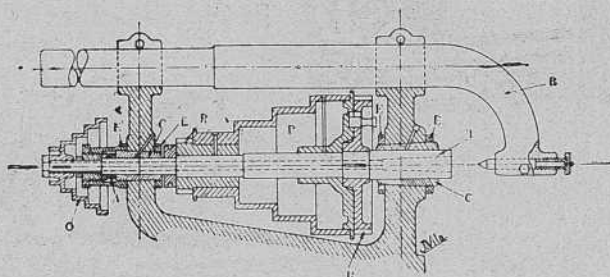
Detalle del cabezal de una fresadora. *B*, brazo; *T*, eje; *C*, cojinetes *E*, tuercas para ajustar los cojinetes; *P*, polea de escalones; *R*, retardo; *O*, polea de avances.
